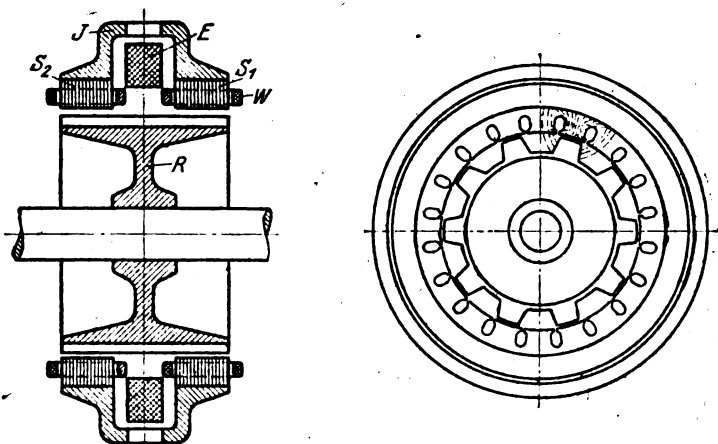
Als Mittel- und Hochfrequenzmaschine ausgebildete Gleichpolmaschine.
